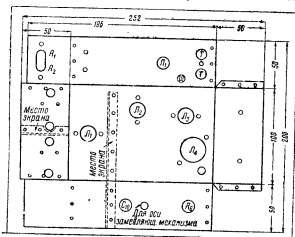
Развертка шасси приемника с указанием расположения и мест крепления основных деталей
